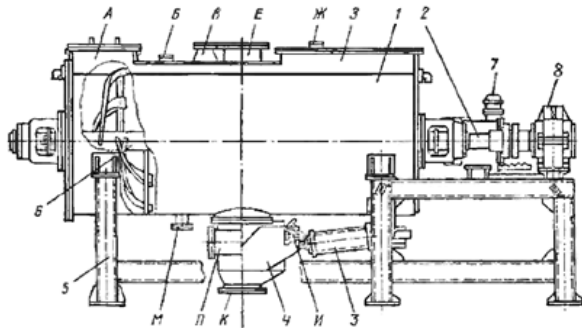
Стрічковий змішувач: 1 – корпус; 2 – вал; 3 – пневмоциліндр; 4 – розвантажувальна коробка; 5 – станина; 6 – перемішувальний пристрій; 7 – електродвигун
